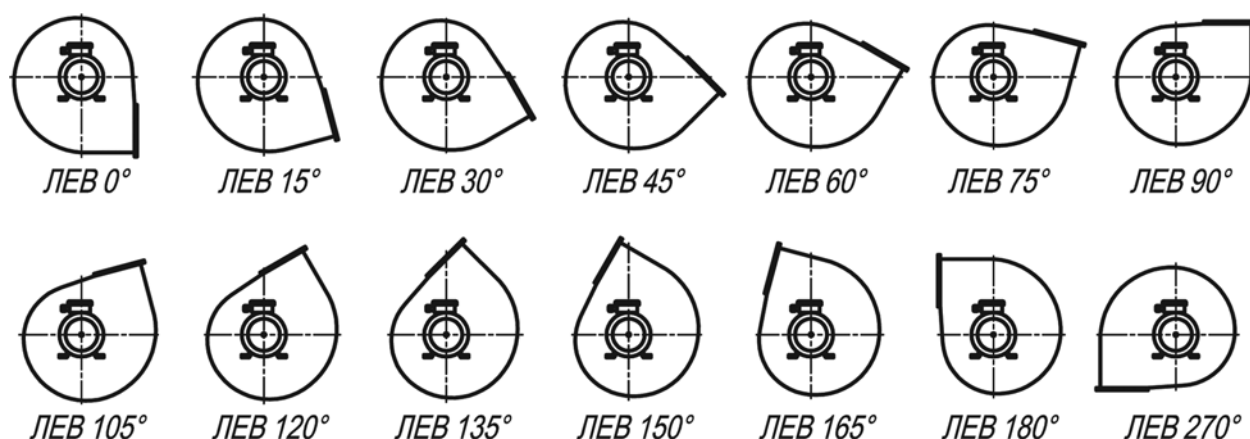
Положение корпуса тягодутьевых машин типа ВД и Д (ЛЕВ).
